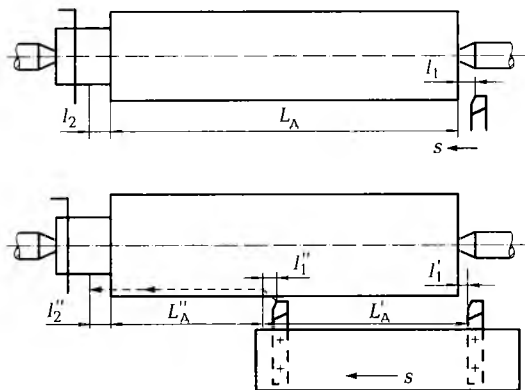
Схемы обработки одной поверхности детали несколькими инструментами
